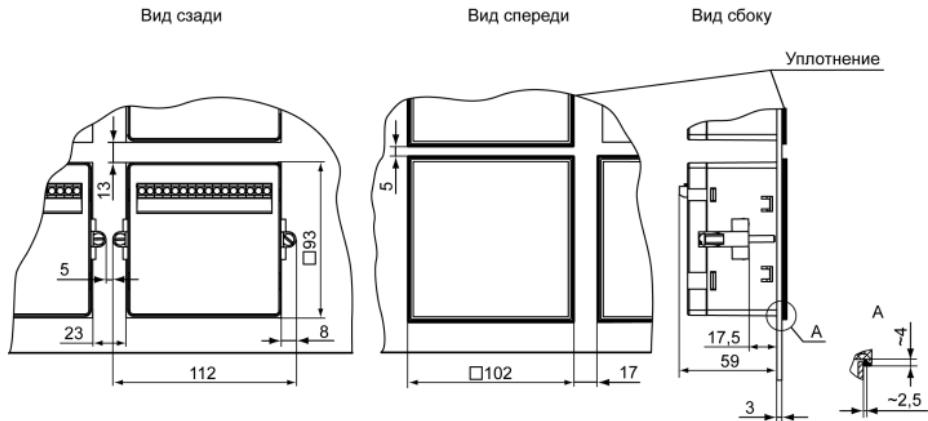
Прибор в корпусе Щ1, установленный в щит толщиной 3 мм
